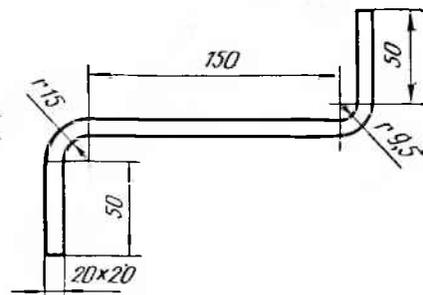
Заготовка квадратного сечения, изогнутая в двух местах
